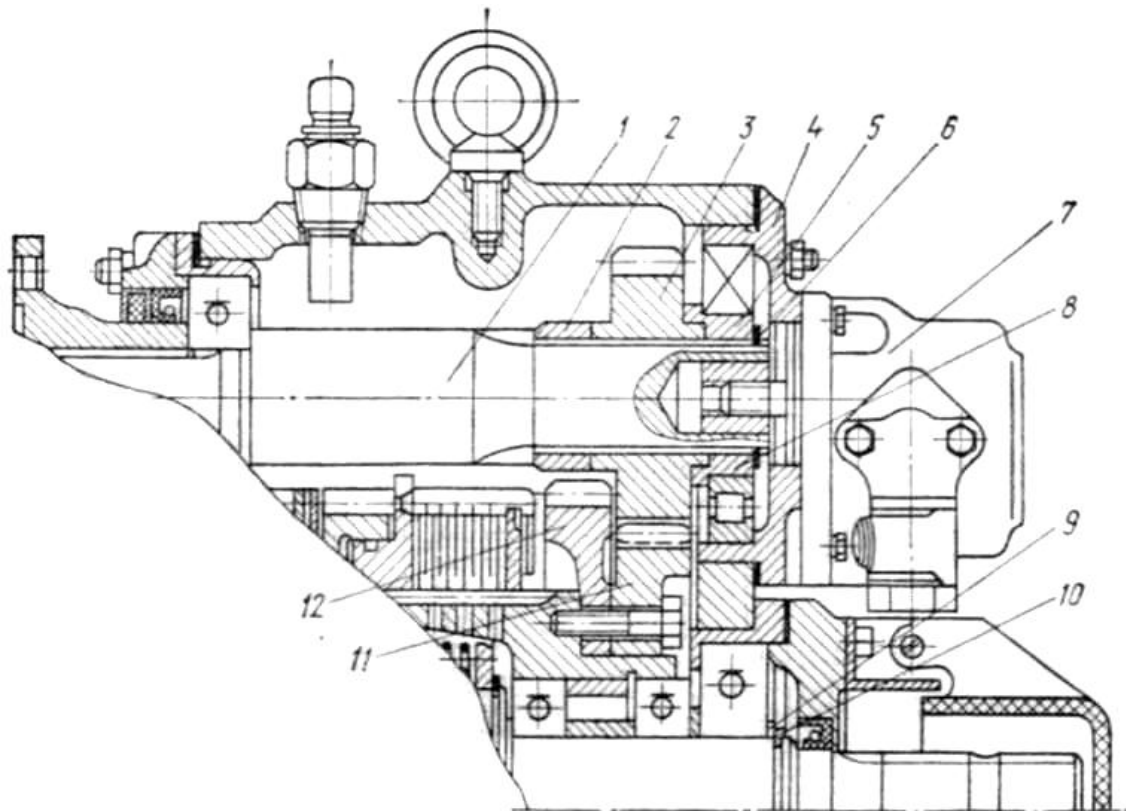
Редуктор ВВП з дВВПа веденими шестернями:
